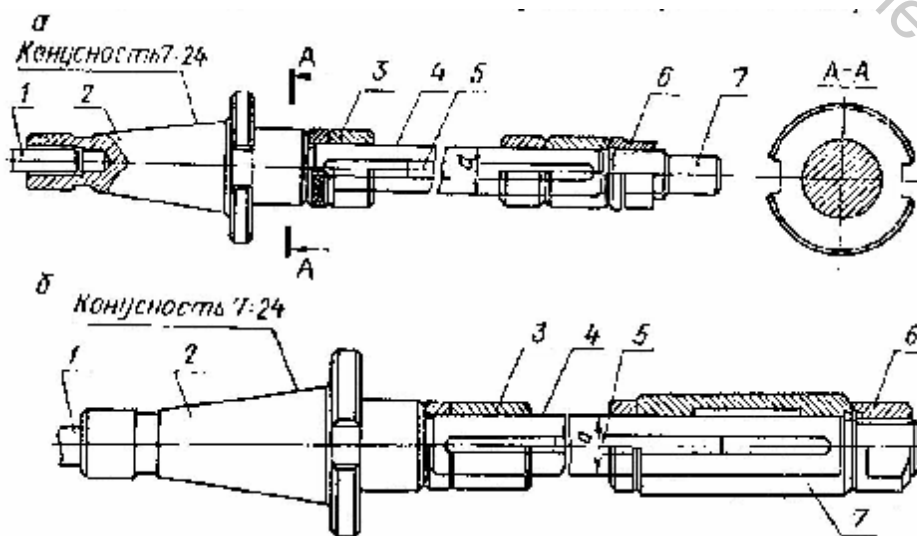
Центровые оправки: с направляющей цангой (а) и с поддерживающей вращающейся буксой (б)
